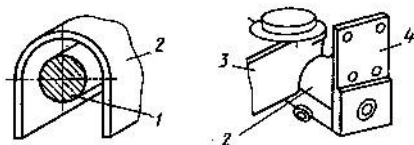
К U-образному профилю 2, служащему балкой подвески на моделях «Ауди», приварены с обеих сторон фланцы 4 опор подшипника колеса и нагруженные на изгиб продольные рычаги 3. Если стабилизирующего действия U-образного профиля недостаточно, дополнительно может быть приварен круглый стержень 1
